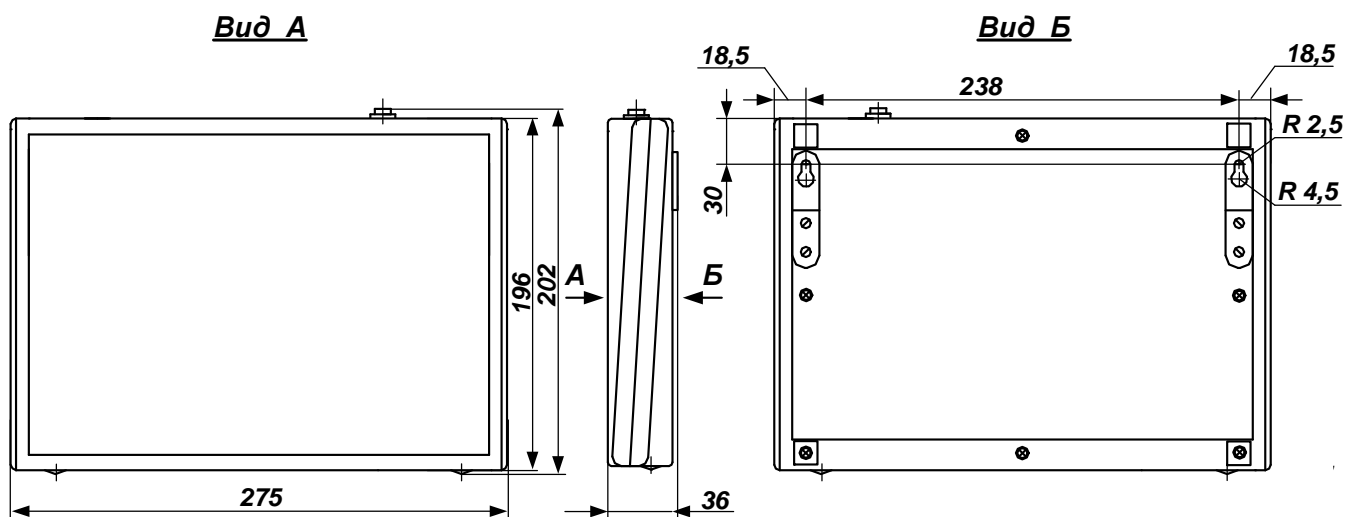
Внешний вид, габаритные и присоединительные размеры
